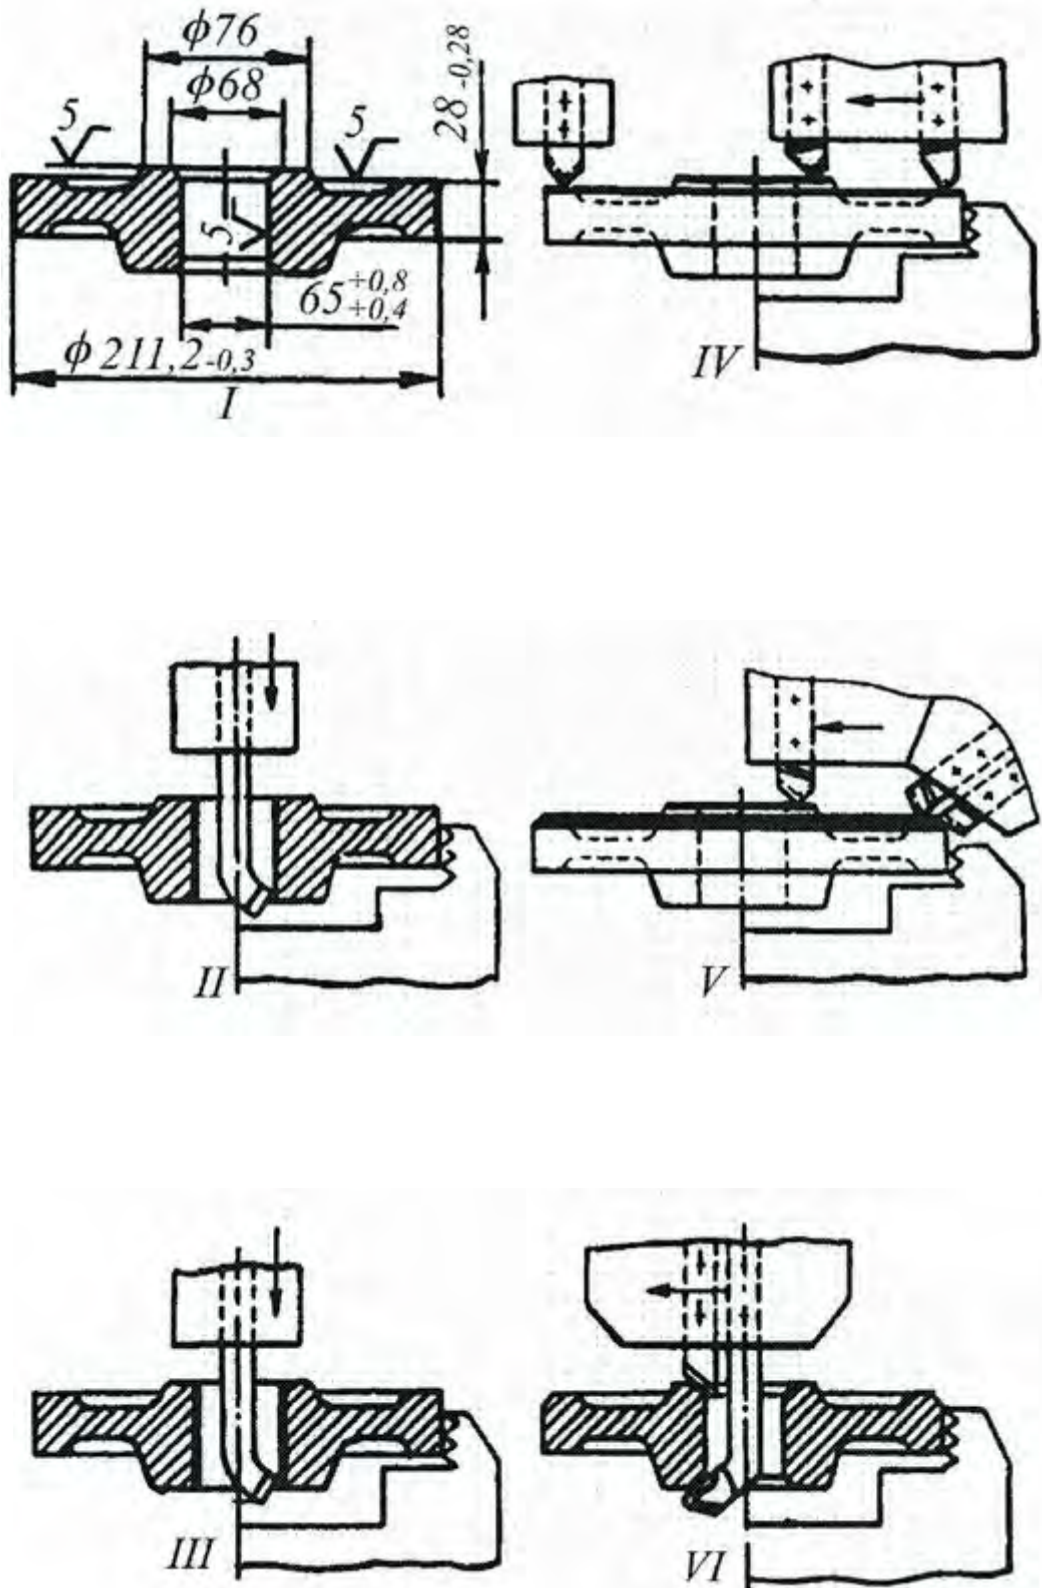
Налаштування вертикального шестишпindelного напівавтомата для виготовлення шестерні
